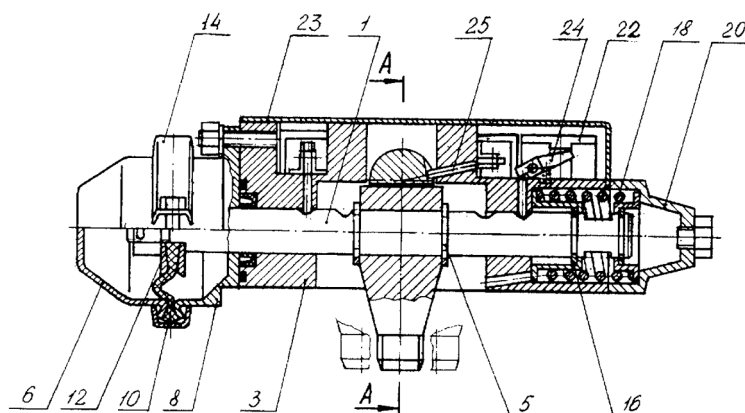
Диафрагменный механизм переключения передач: 1 — шток; 3 — корпус; 5 — стопорное кольцо; 6, 8 — корпус пневмокамеры; 10 — диафрагма; 12 — тарелка; 14 — крепление; 16 — стакан; 18 — возвратная пружина; 20 — корпус позиционного устройства; 22, 24, 25 — датчики; 23 — крышка
